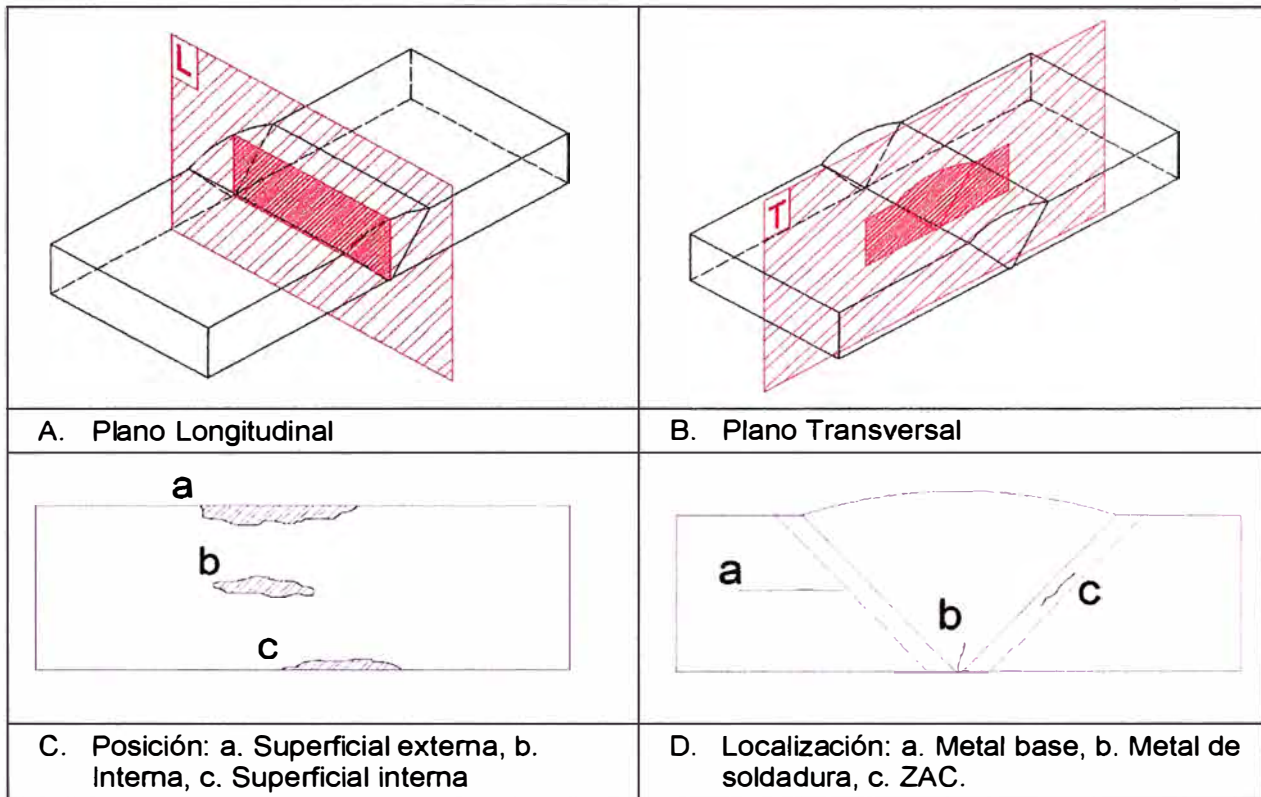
Descripción de una discontinuidad plana en una unión soldada.
